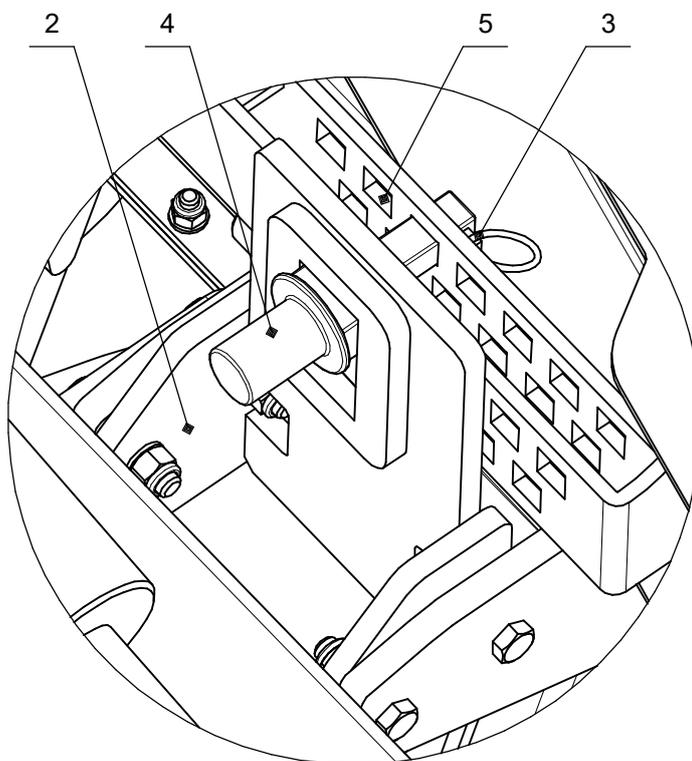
Регулировка смещения дисковых рядов дисковой почвообрабатывающей машины ДПМ-5000, ДПМ-6000
